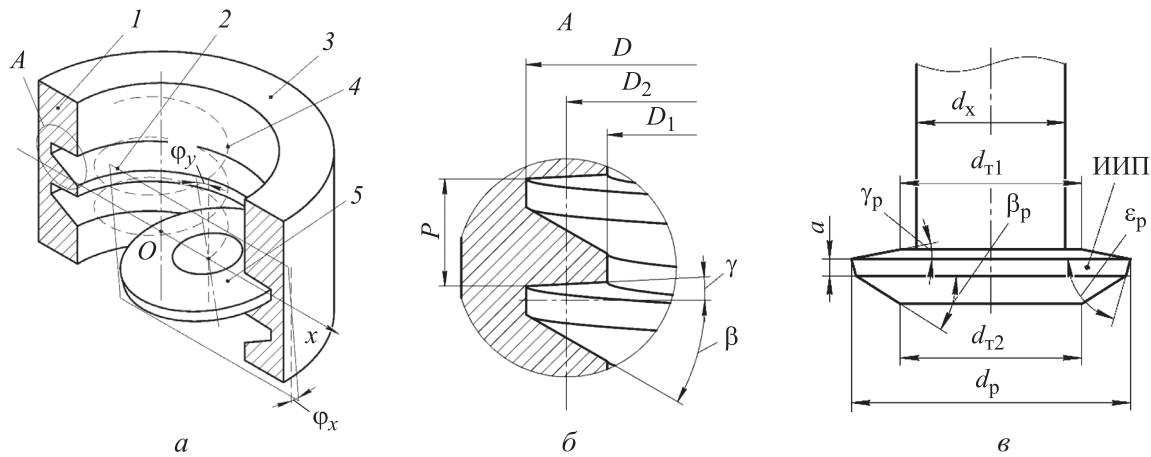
Параметры моделирования резбобфрезерования заготовки:
